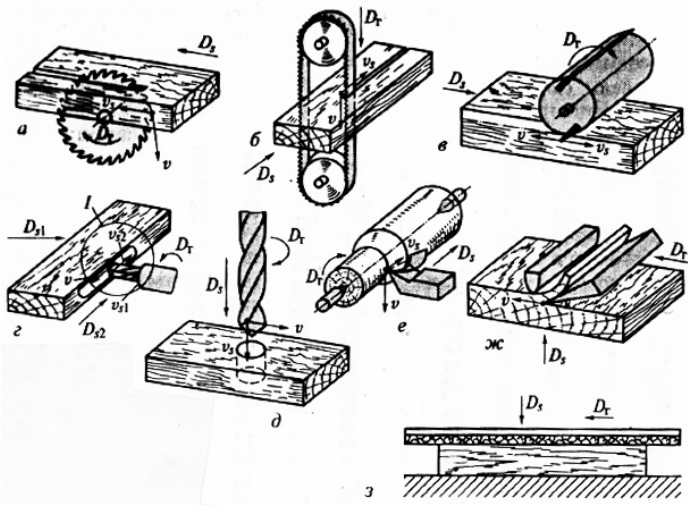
Процессы резания древесины: а – пиление круглой пилой; б – пиление ленточной пилой; в – фрезерование; з – пазовое фрезерование концевой фрезой; д – сверление; е – точение; ж – строгание; з – шлифование
